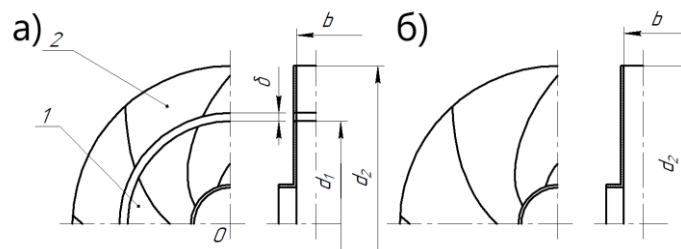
Центробежный насос а) стандартной конструкции; б) с соосным расположением рабочих колес: 1 - внутреннее рабочее колесо, 2 - наружное рабочее колесо, δ - радиальный зазор, b - ширина колеса, d_1, d_2 - внешние диаметры внутреннего и наружного рабочих колес
